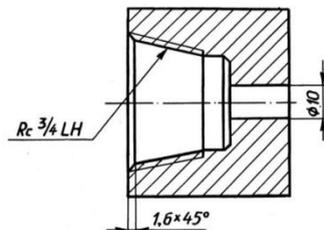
Обозначение внутренней трубной конической резьбы
